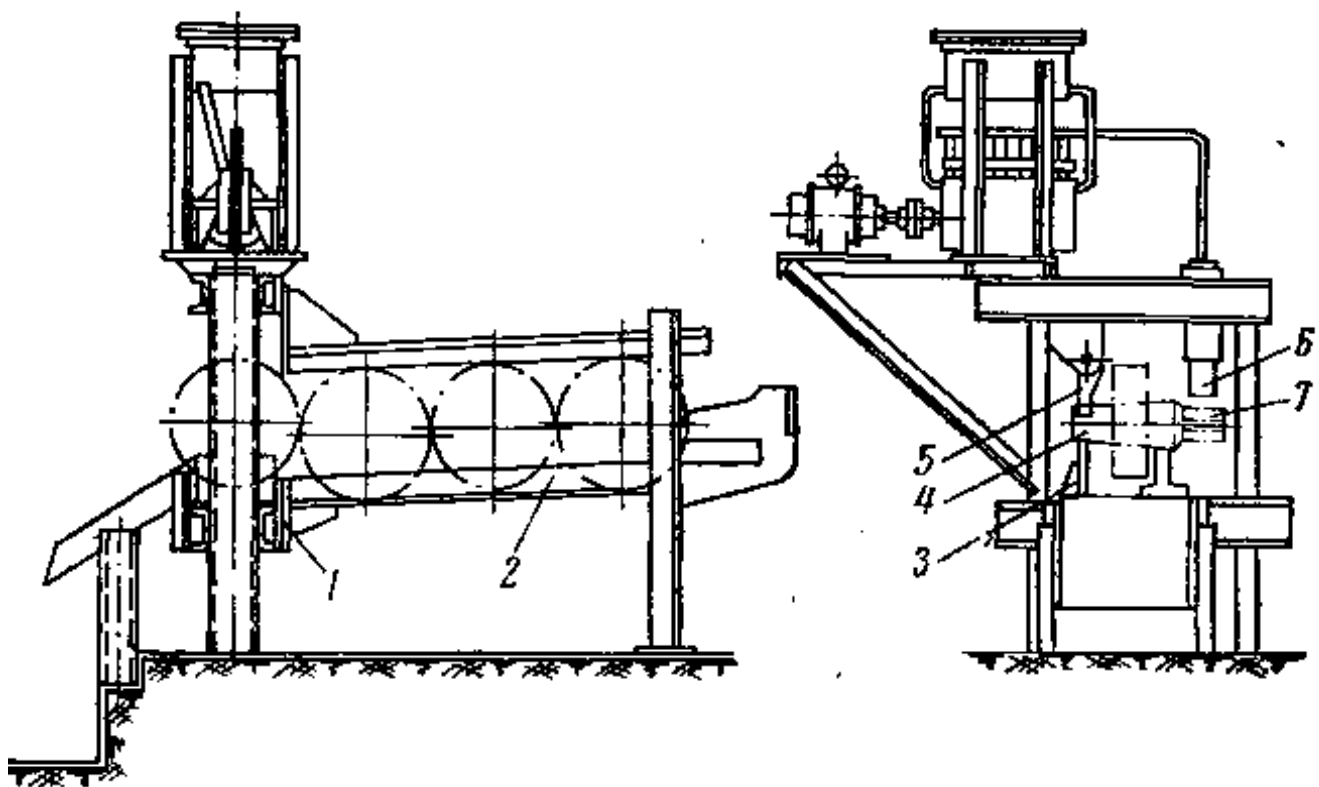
Пресс для ломки прибылей отливки ступицы
